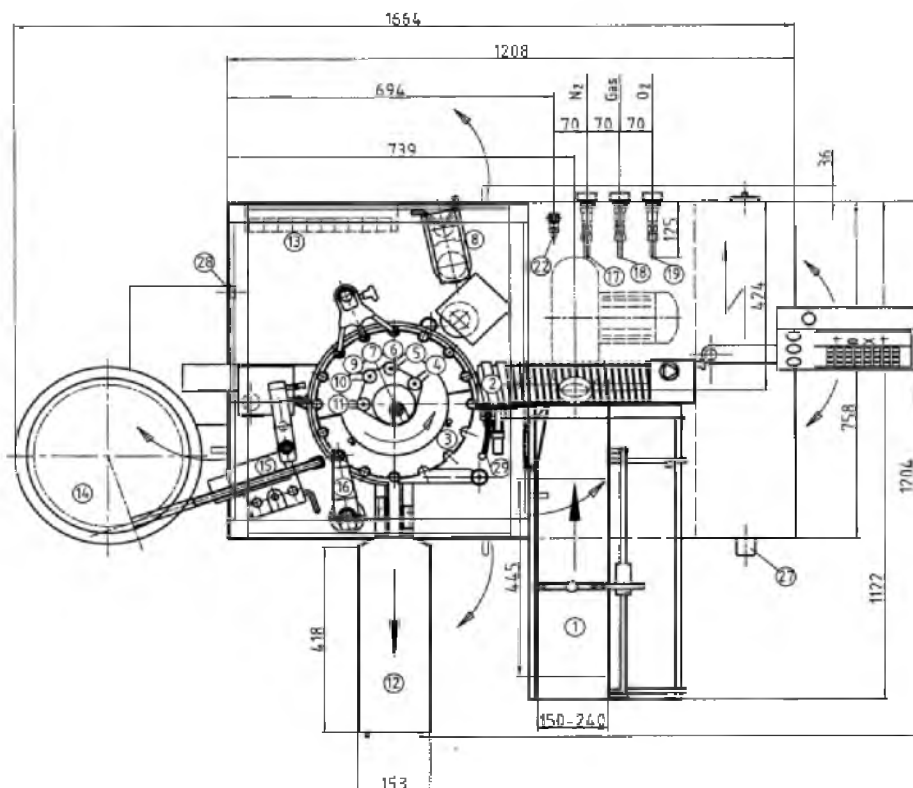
Partes de la máquina llenadora y selladora de ampolletas (ROTA, 2011).
